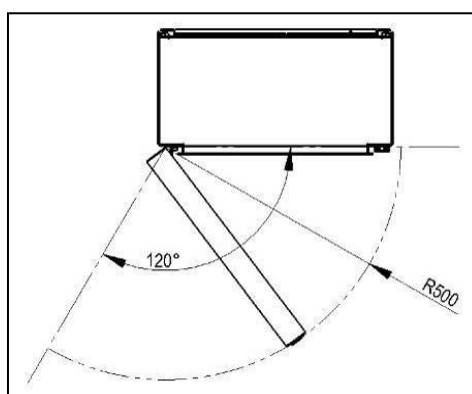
Dimensiones del Gabinete SAS - Apertura de puerta
